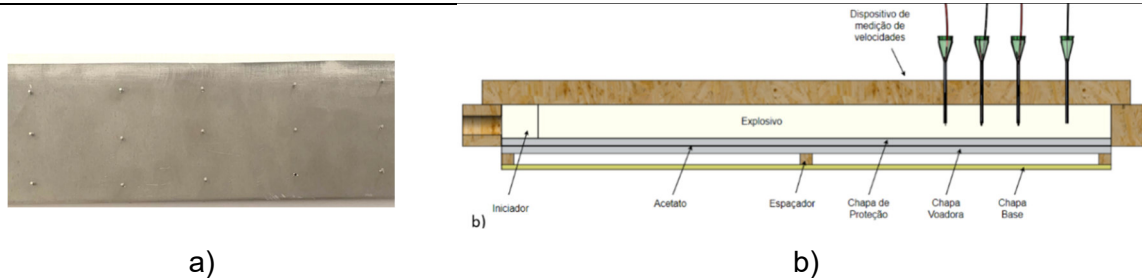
(a) Chapa de alumínio com grampos; (b) Montagem experimental utilizada.
